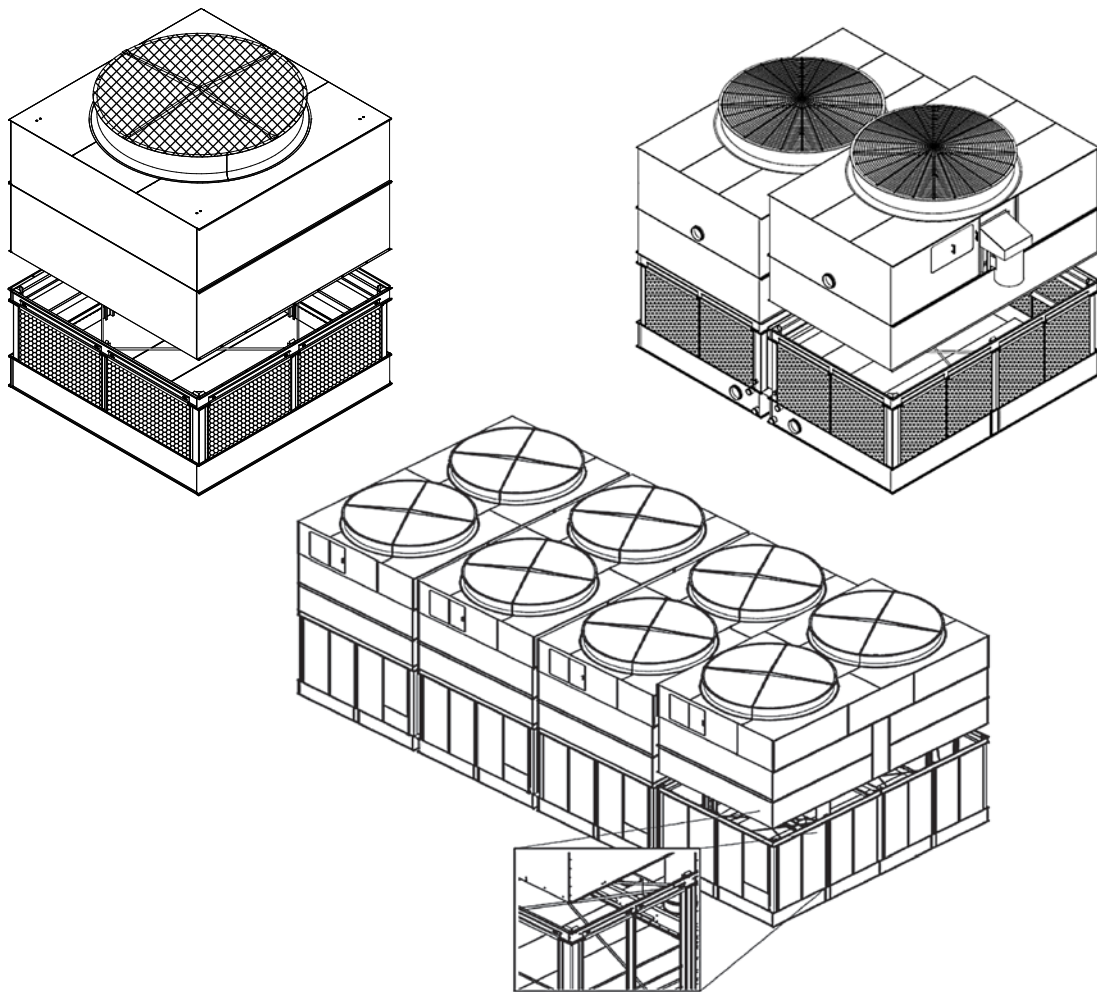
Assemblaggio della sezione ventilante con la sezione bacino –
